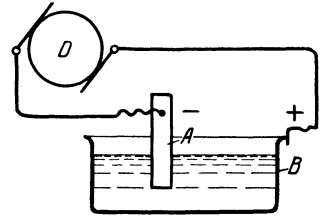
Schweißung mittels Elektrolyse.
